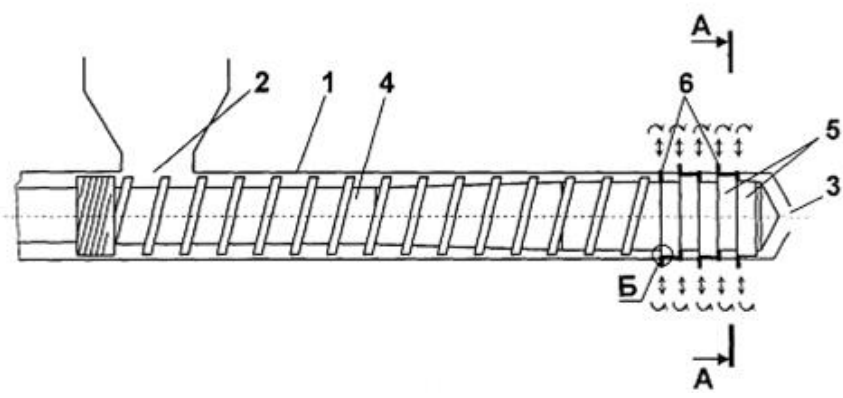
Поздовжній переріз черв'ячного екструдера
